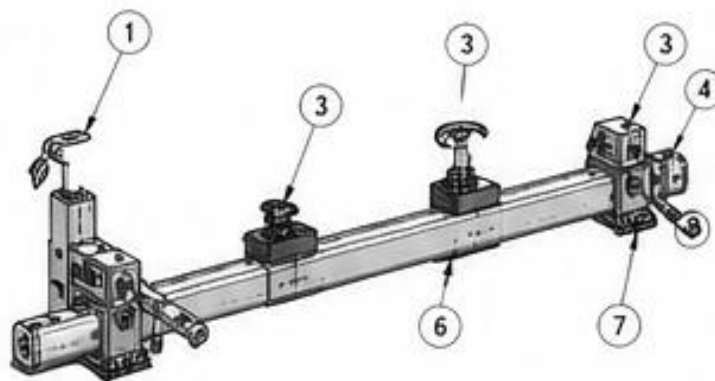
Загальний вигляд контрольного пристосування
